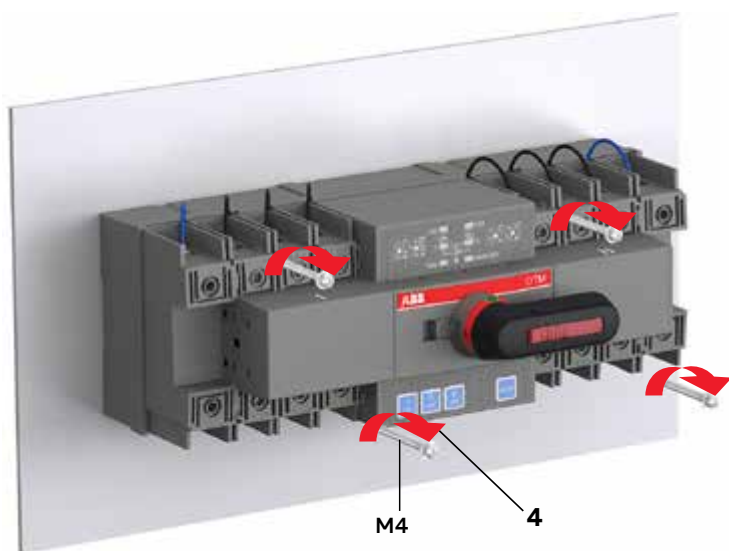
Installation von OTM_C_21D, mit Schrauben auf Montageplatte
